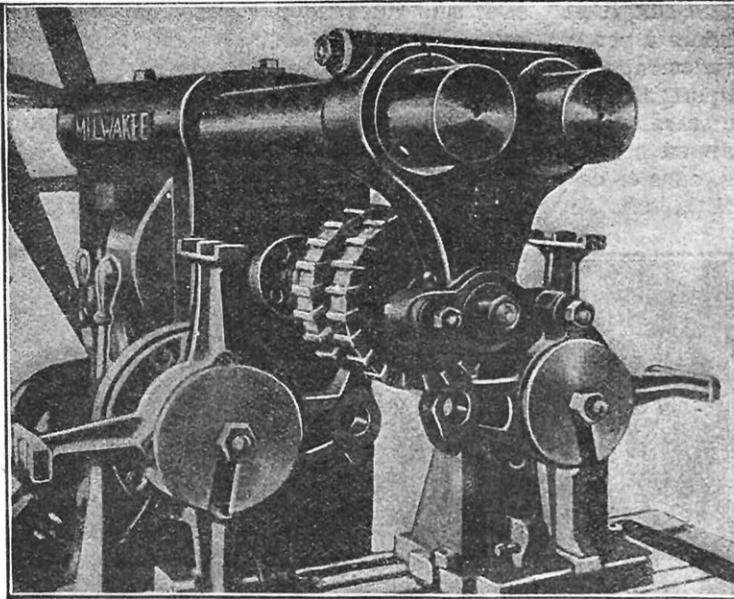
MACHINE A FRAISER PERFECTIONNÉE
